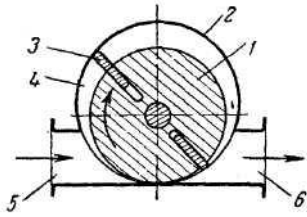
Схема пластинчастого роторного насоса: 1 – ротор; 2 – корпус; 3 – пластини; 4 – робочий простір; 5 – всмоктувальний патрубок; 6 – нагнітальний патрубок
